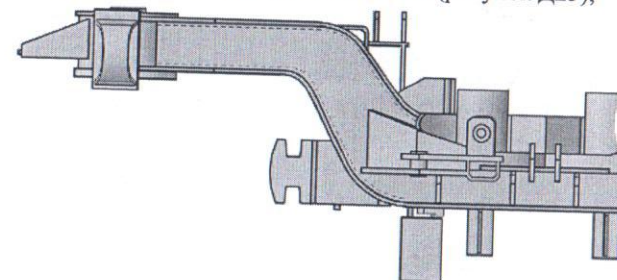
Контроль околошовных зон сварного соединения боковых стенок продольных балок рамы с верхним и нижним поясом
